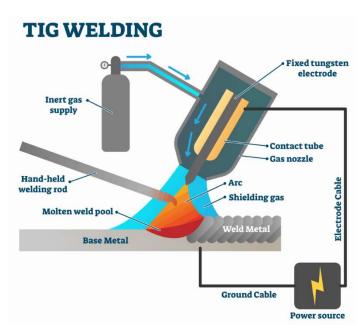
Esquema de soldadura TIG (Technox Machine)
